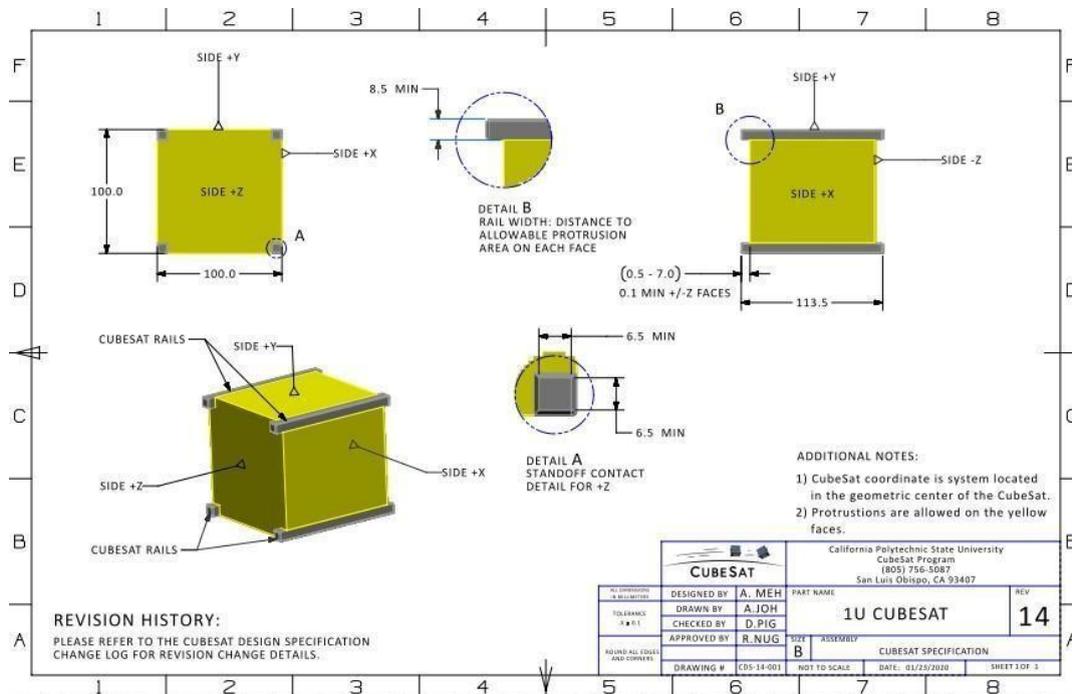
Чертеж спутника формфактора кубсат 1u
